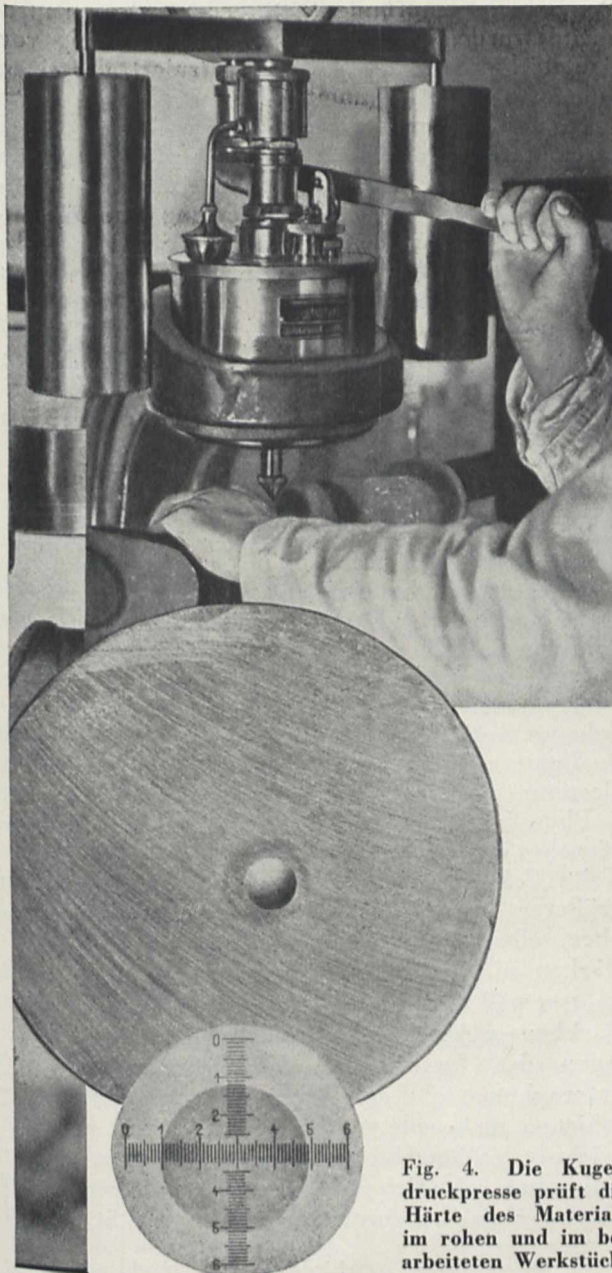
Die Kugeldruckpresse prüft die Härte des Materials im rohen und im bearbeiteten Werkstück.
